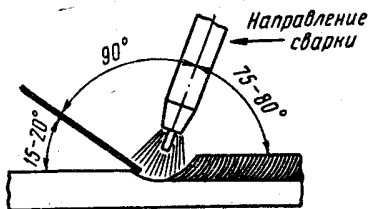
Схема расположения присадочной проволоки и горелки по отношению к свариваемому изделию
